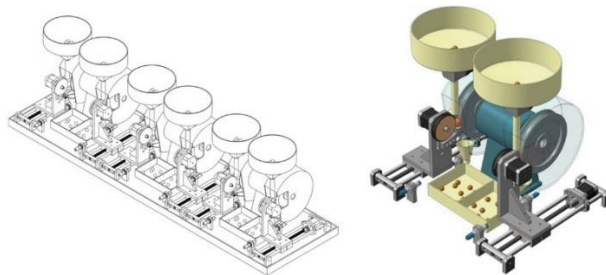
Компоновка багатопозиційного верстата-автомата паралельної дії: а – загальний вид верстата, що складається з 3-х секцій; б – загальний вид однієї секції верстата
